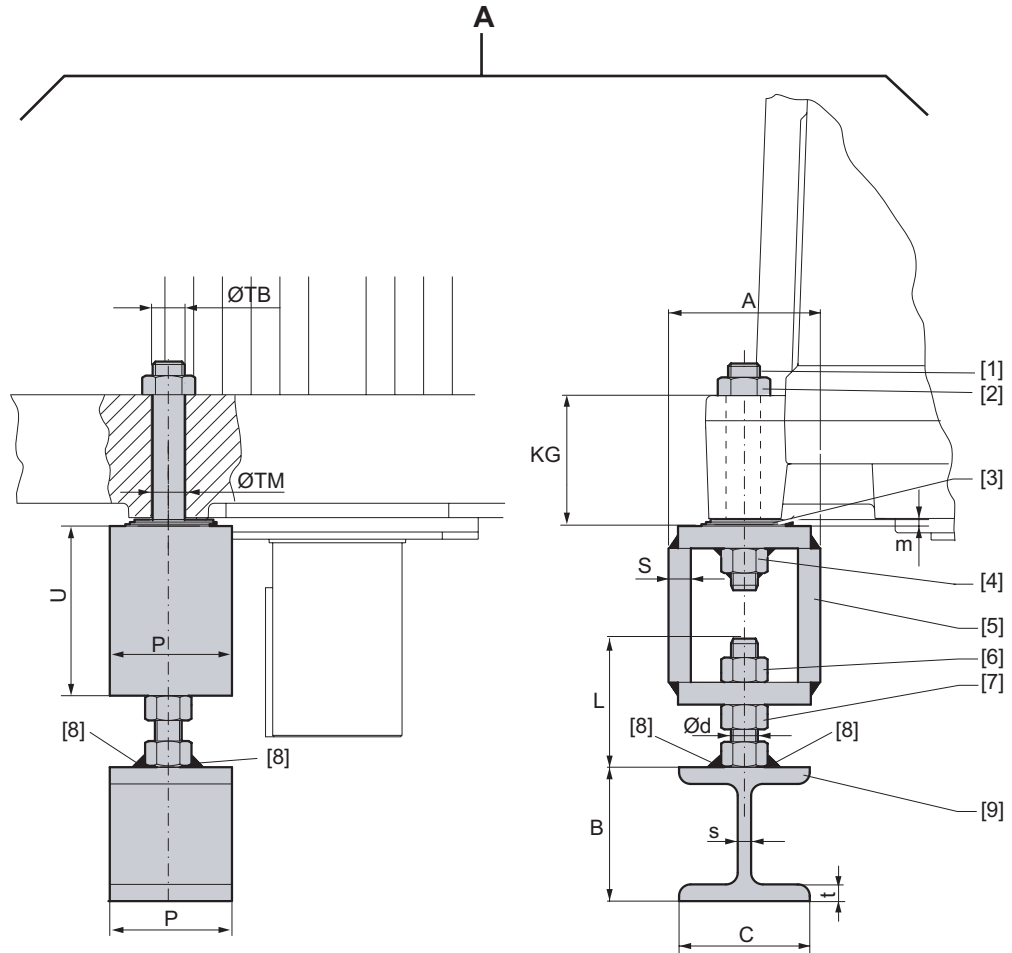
Армирование нижнего слоя фундамента (поз. "А") редукторов M.V.. 60...90
